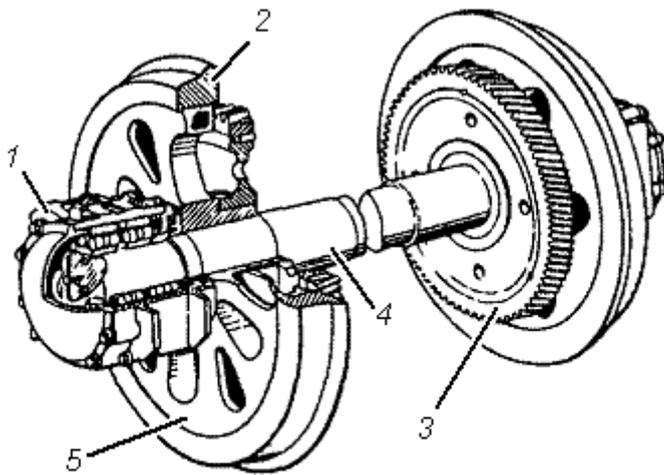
Колесная пара электровоза: 1 – корпус буксы; 2 – бандаж; 3 – зубчатое колесо; 4 – ось; 5 – колесный центр
